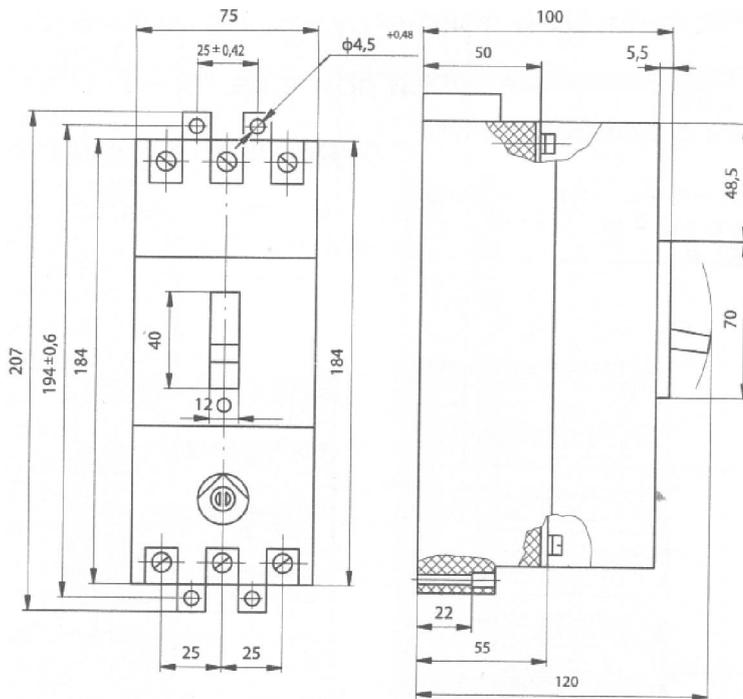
Габаритные размеры выключателя АЕ-2046
